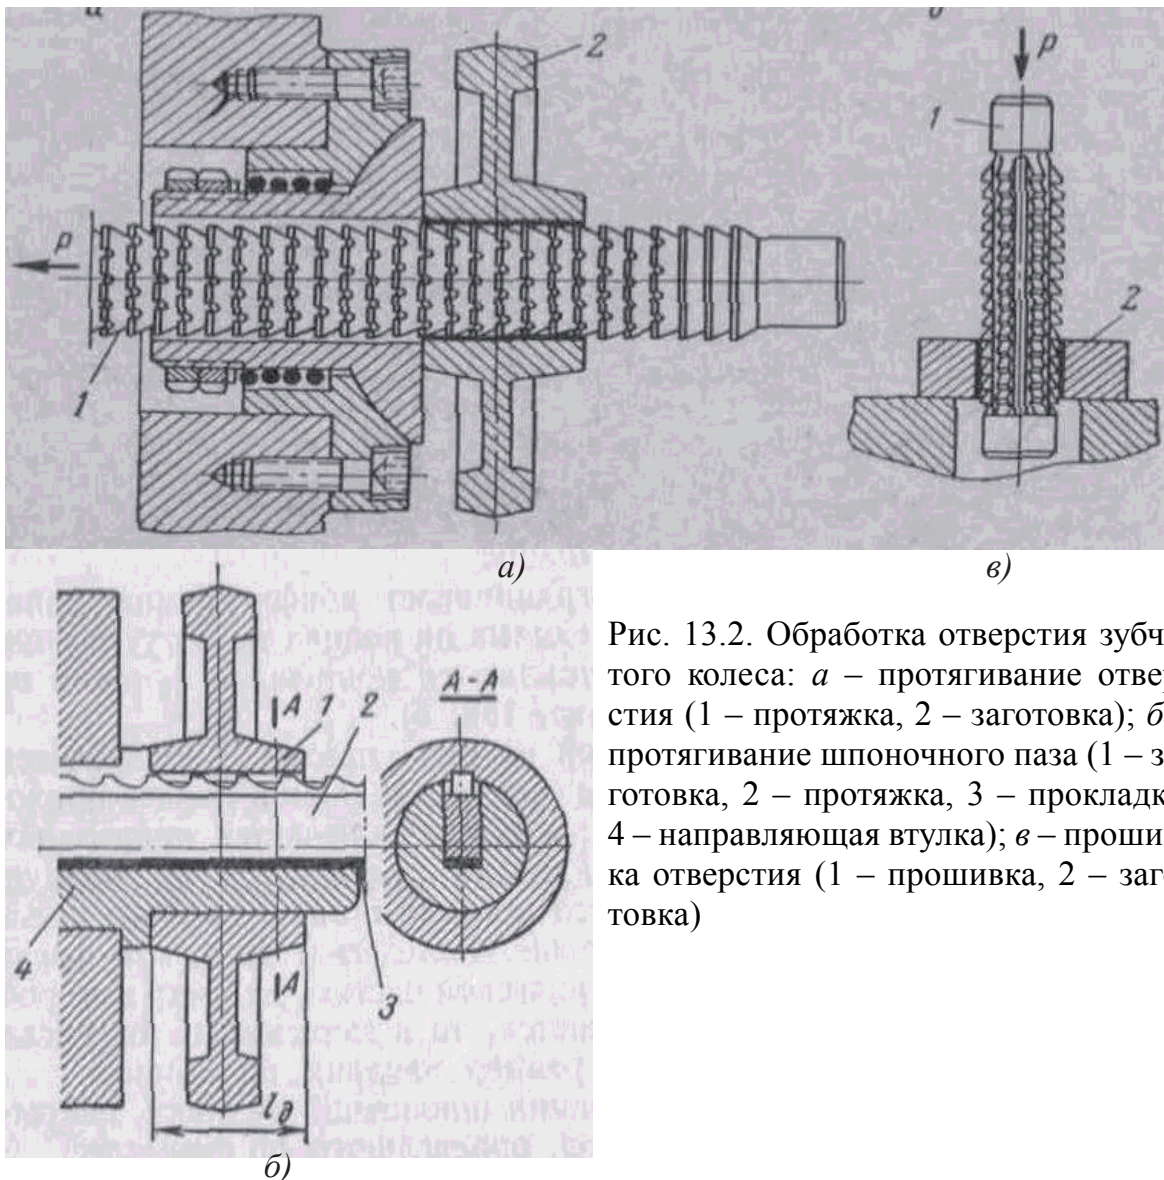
Обработка отверстия зубчатого колеса: а – протягивание отверстия (1 – протяжка, 2 – заготовка); б – протягивание шпоночного паз (1 – заготовка, 2 – протяжка, 3 – прокладка, 4 – направляющая втулка); в – прошивка отверстия (1 – прошивка, 2 – заготовка)
